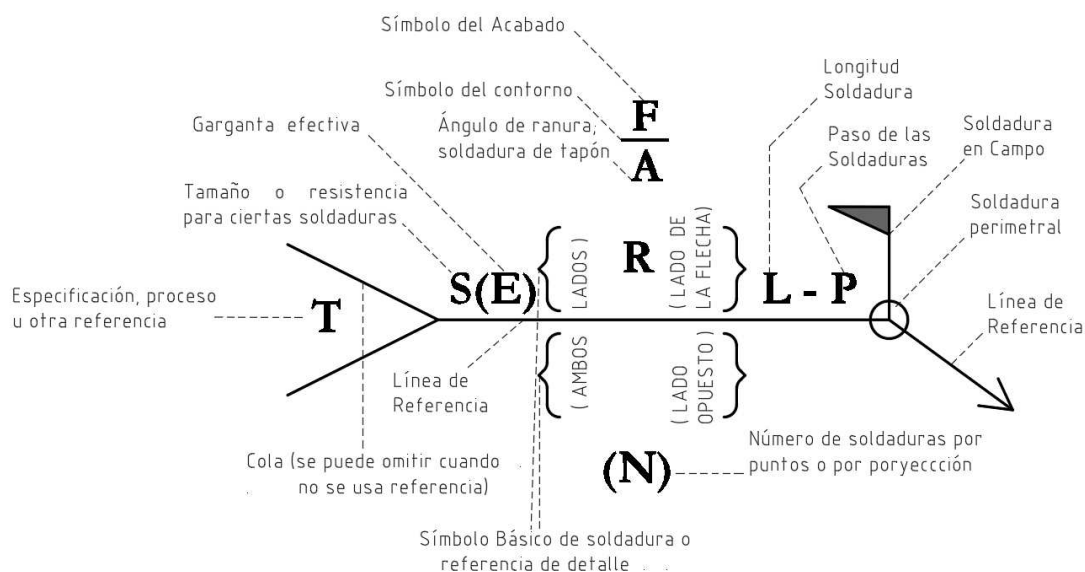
Posición de los elementos de un símbolo de soldadura
